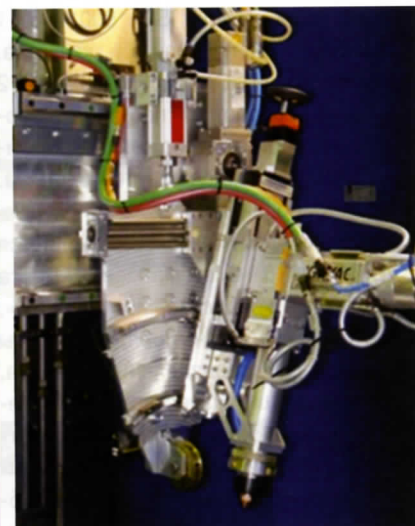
Линия изготовления плоских секций с использованием лазерной резки и гибридной лазерно-дуговой сварки
